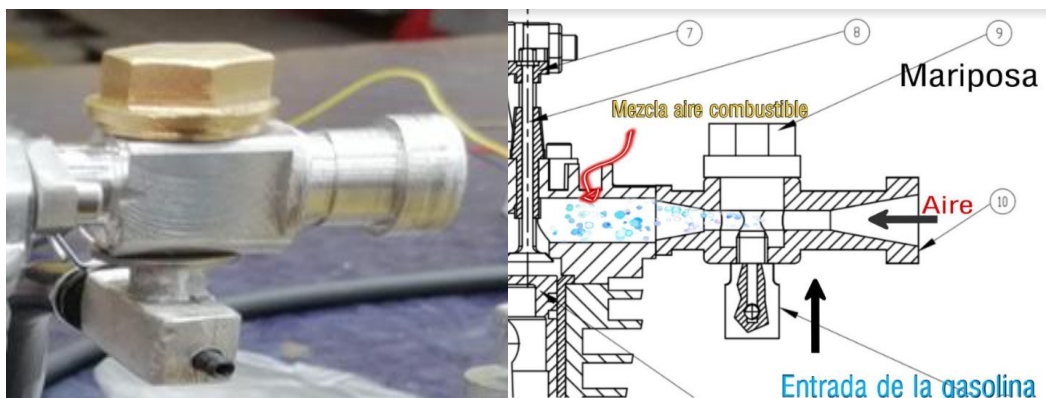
Carburador elemental, adaptado para el prototipo de motor de combustión interna. [32]
